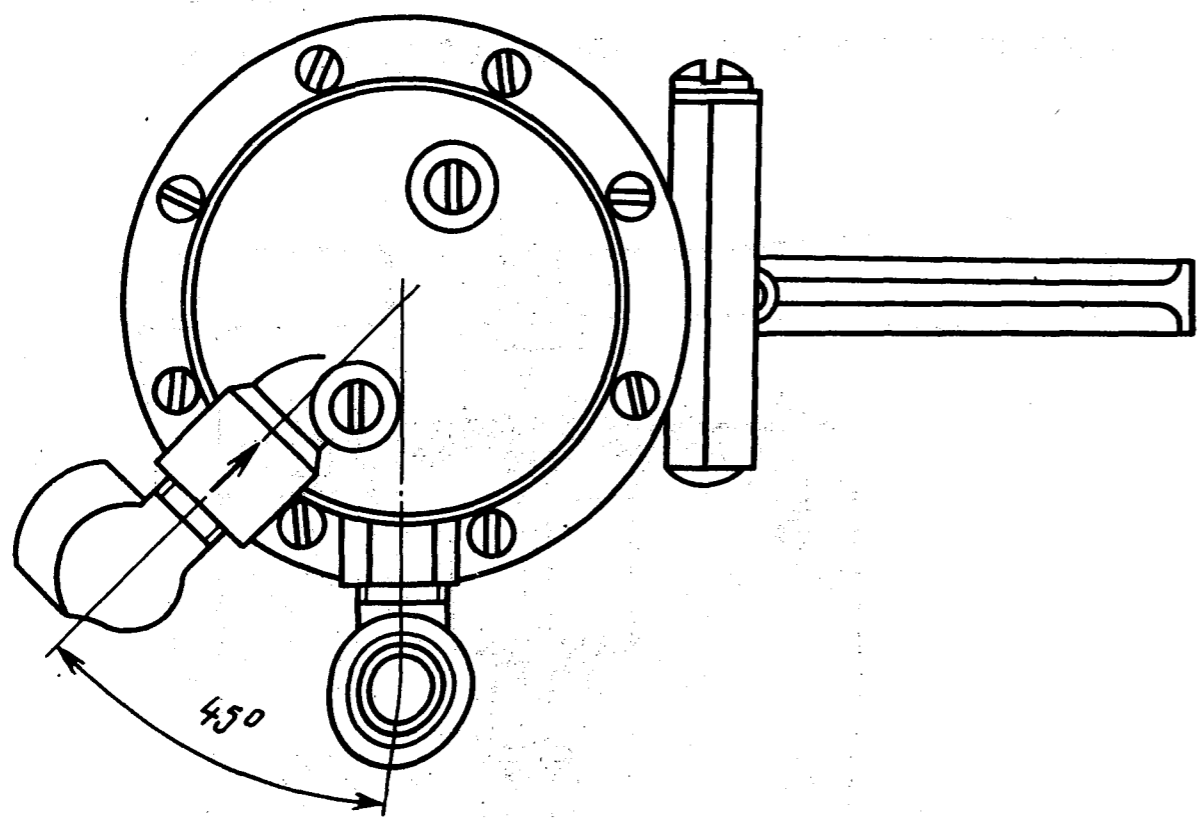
Положение головки и крышки бензинового насоса относительно корпуса
